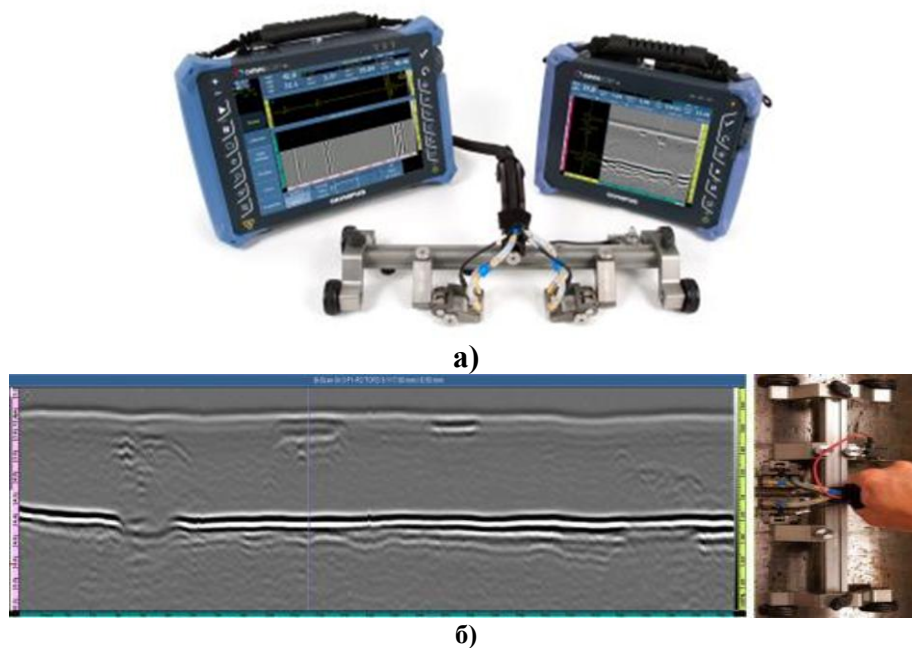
Обладнання для реалізації ДЧМ контролю зварного з'єднання:
